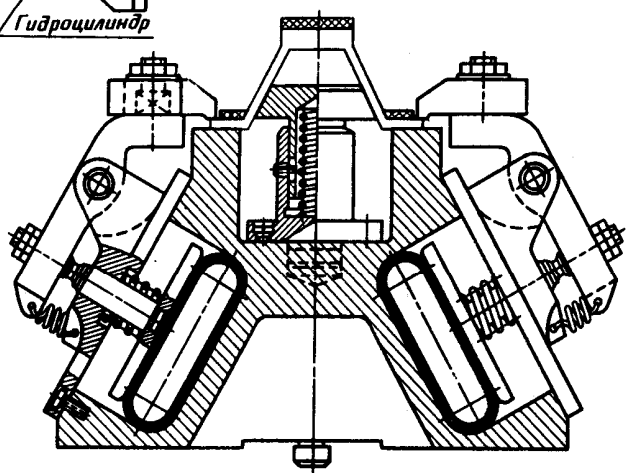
Приспособление с силовыми камерами из дюритовых шлангов
